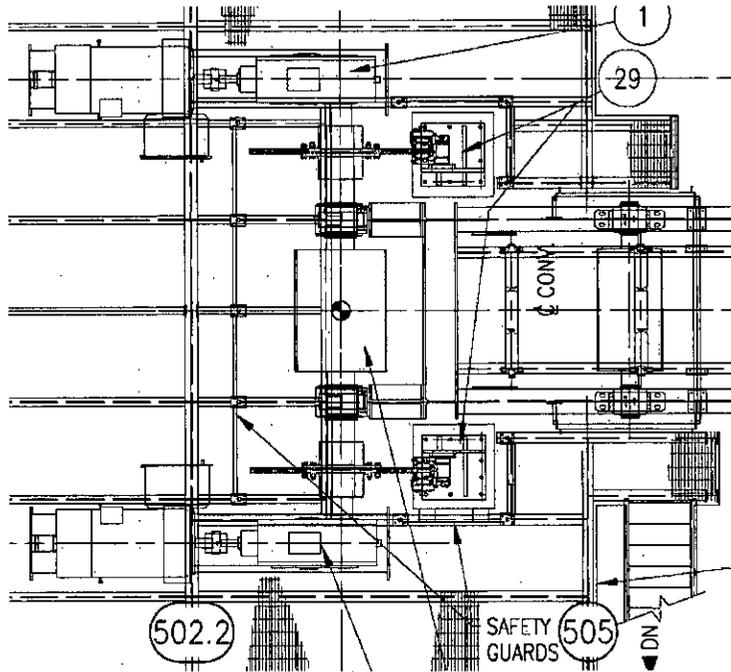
VISTA DE ELEVACION DE LA ESTACION DE ACCIONAMIENTO,
